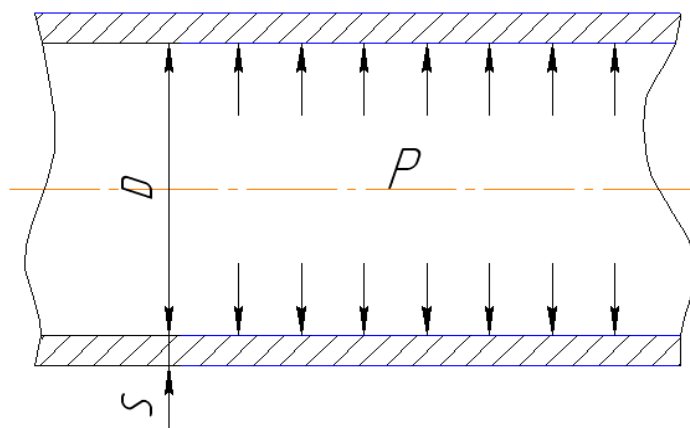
Розрахункова схема циліндричної оболонки
